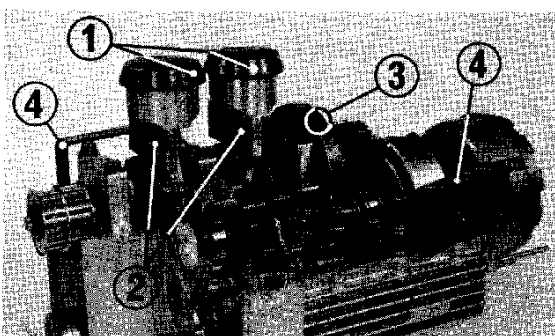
(1) Kolbenring-Einführwerkzeug
